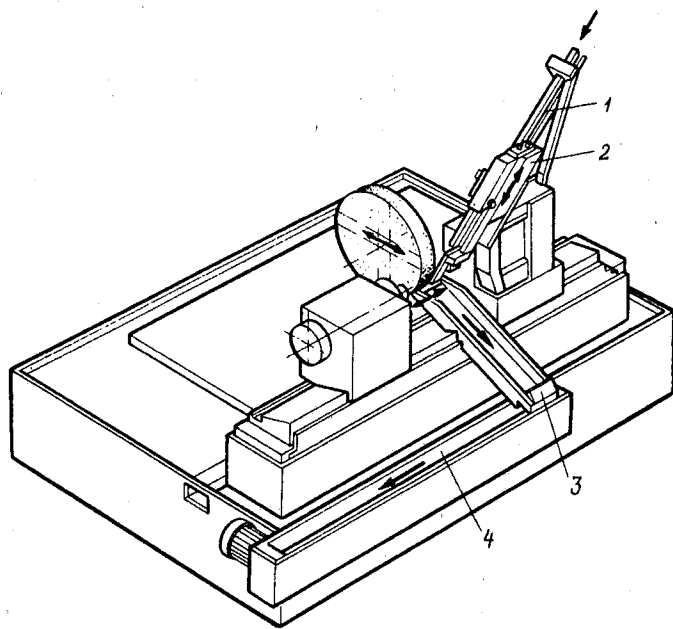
Устройство загрузки — разгрузки круглошлифовального станка
